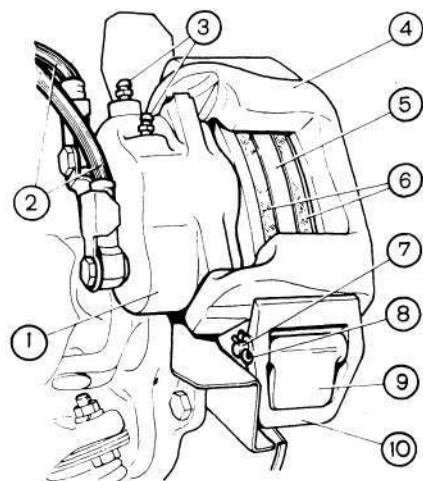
Передний дисковый тормоз: 1 — блок цилиндров; 2 — гибкие шланги; 3 — штуцеры; 4 — суппорт; 5 — тормозной диск; 6 — тормозные колодки; 7 — ось прижимного рычага; 8 — шплинт; 9 — направляющая колодок; 10 — прижимной рычаг
